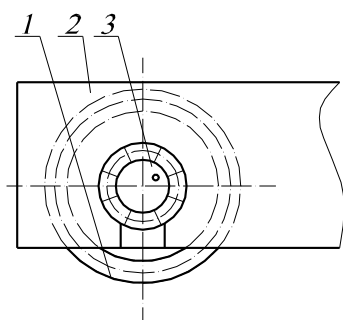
Конструкции ходовой части механизма передвижения крана со встроенными во внутрь колесами: 1 – ходовое колесо; 2 – концевая балка; 3 – крепление ходового колеса к концевой балки
